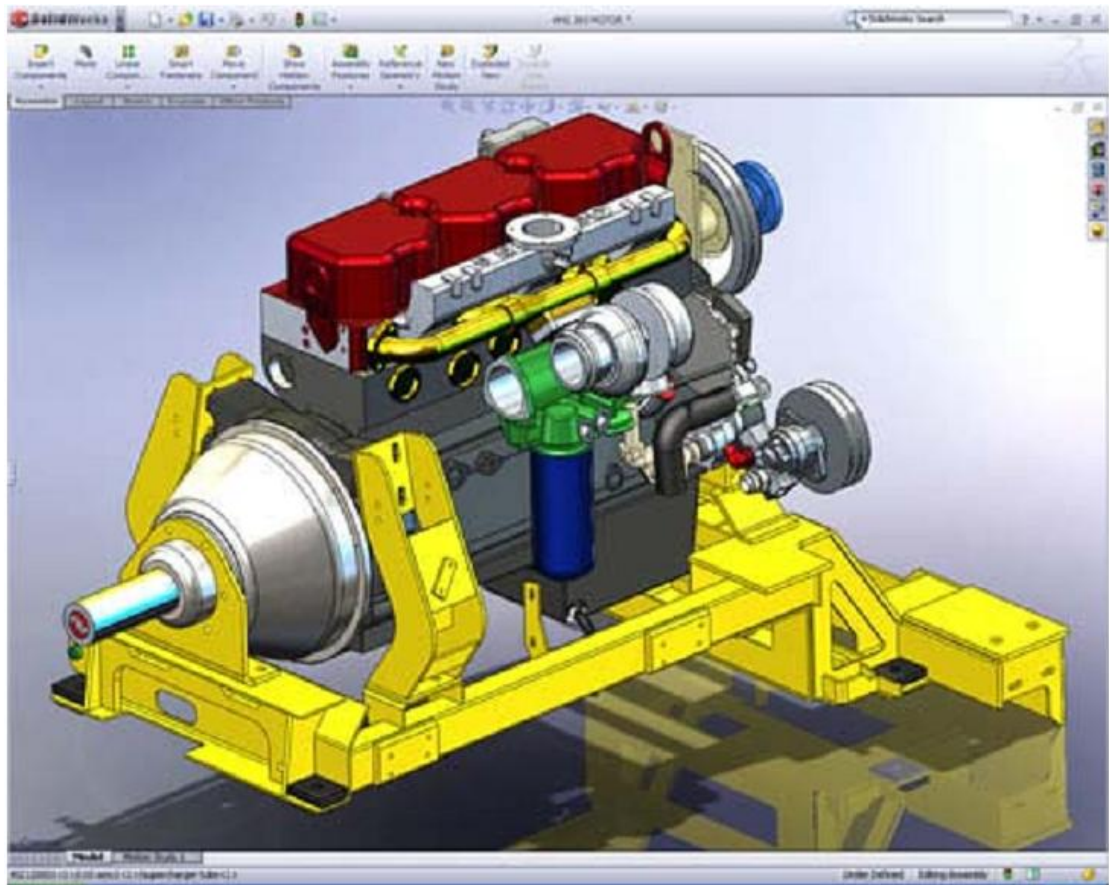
Δημιουργία Part , assembly ,Drawing
